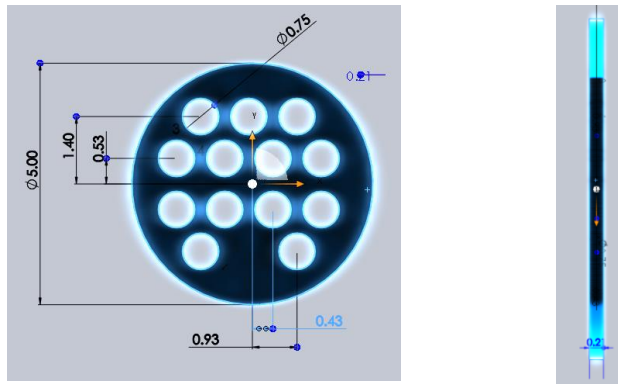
Dimensionamiento del espejo del haz de tubos. Fuente: SolidWorks
